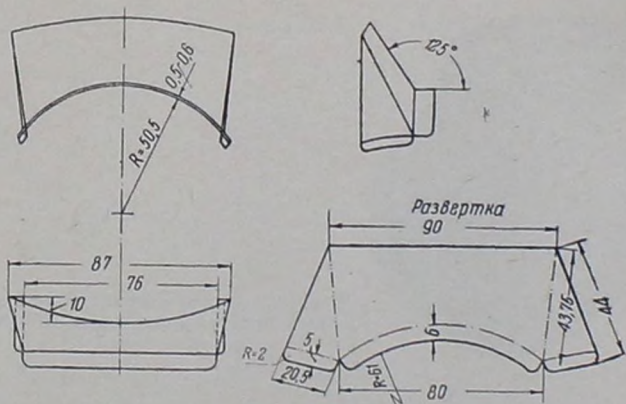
Приспособление для маскировки освещения номерного знака автомашин ЗИС-101:
